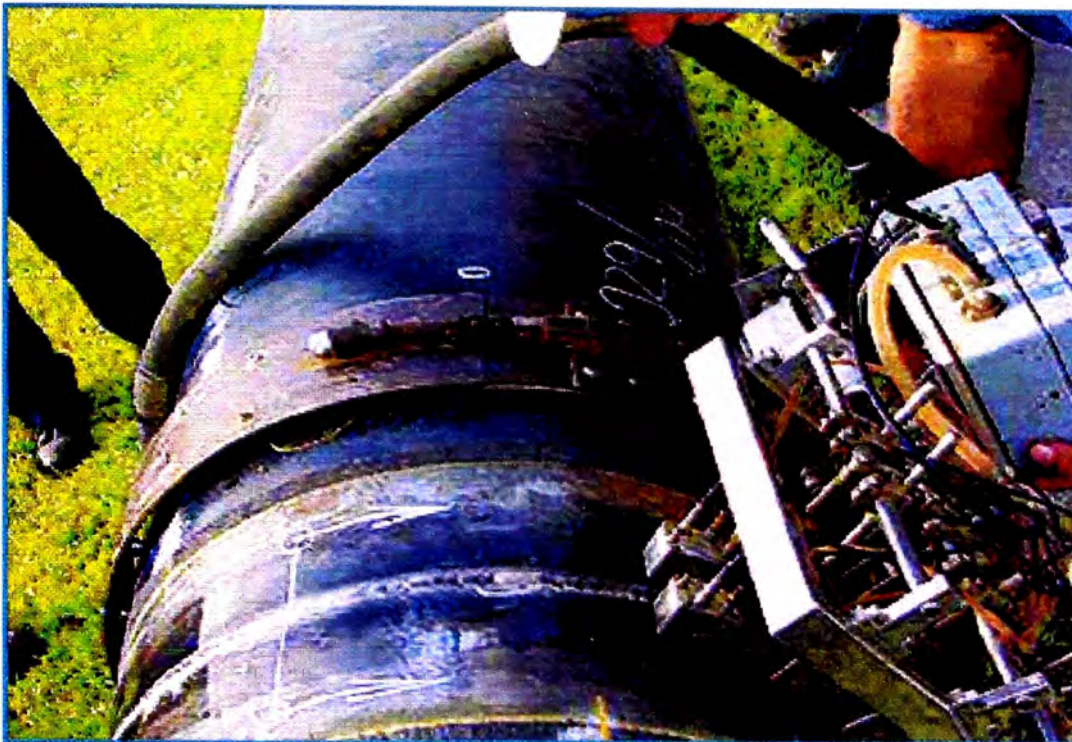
Inspección de soldadura por ultrasonido (Rotoscan), la cual permite verificar la óptima calidad de la soldadura de cada junta
